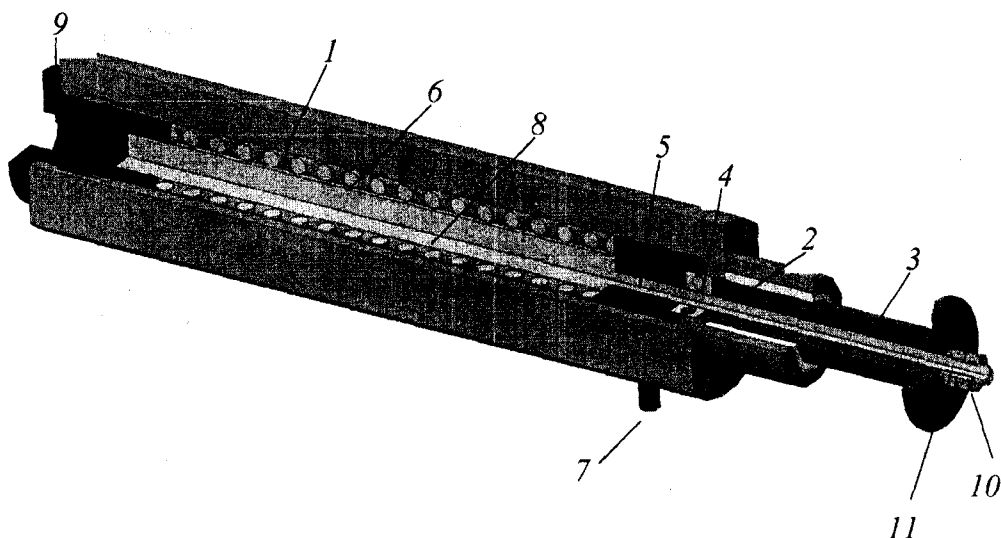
Конструкция инструмента для ОУО ППД ходовых гаек скольжения на токарных станках
